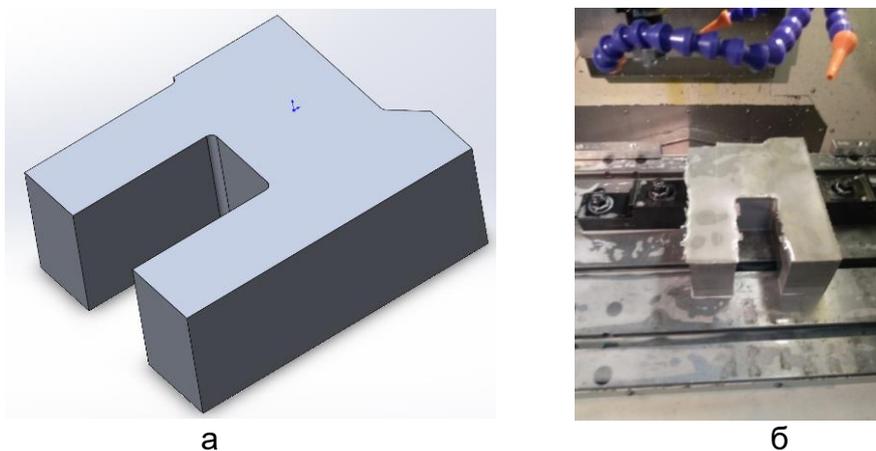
а-Аналітичний еталон заготовки; б-встановлена заготовка
